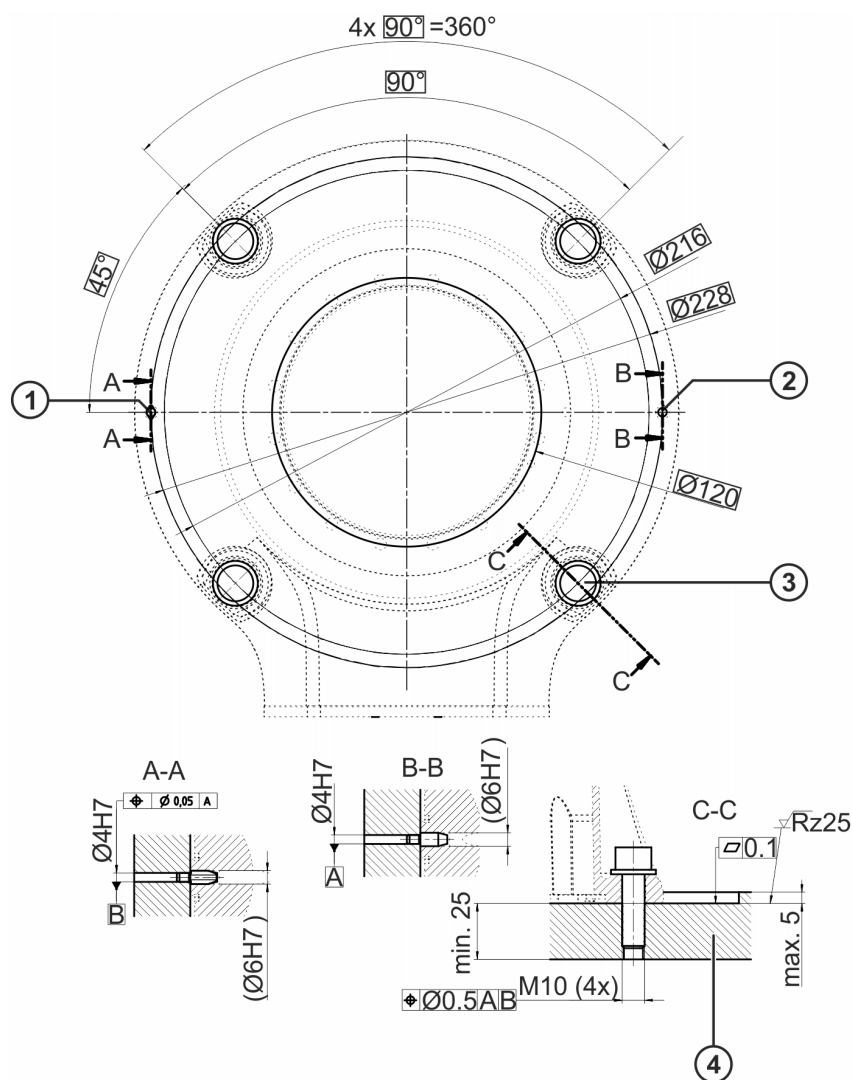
机架固定装置, 尺寸图 LBR iiwa 14 R820
